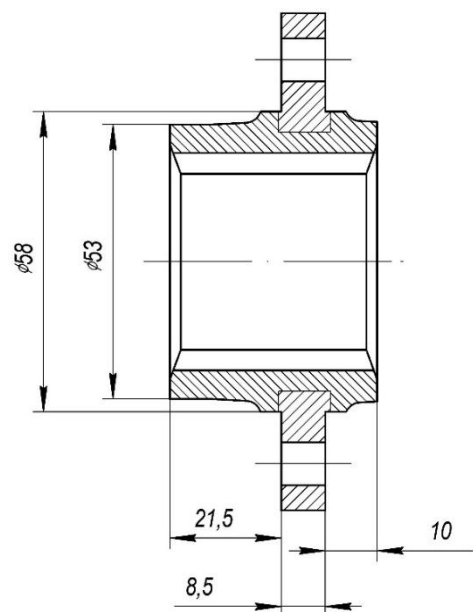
Эскиз детали «ступица» диска сцепления автомобиля
